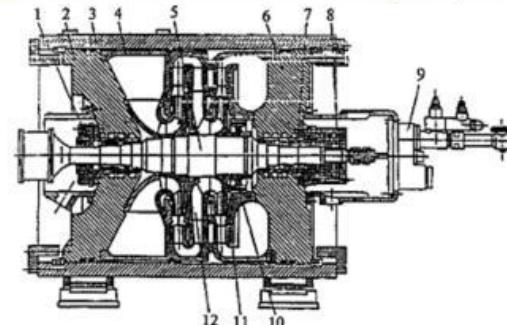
Полнонапорный двухступенчатый нагнетатель НЦ-16/76 агрегата ГПА У16
